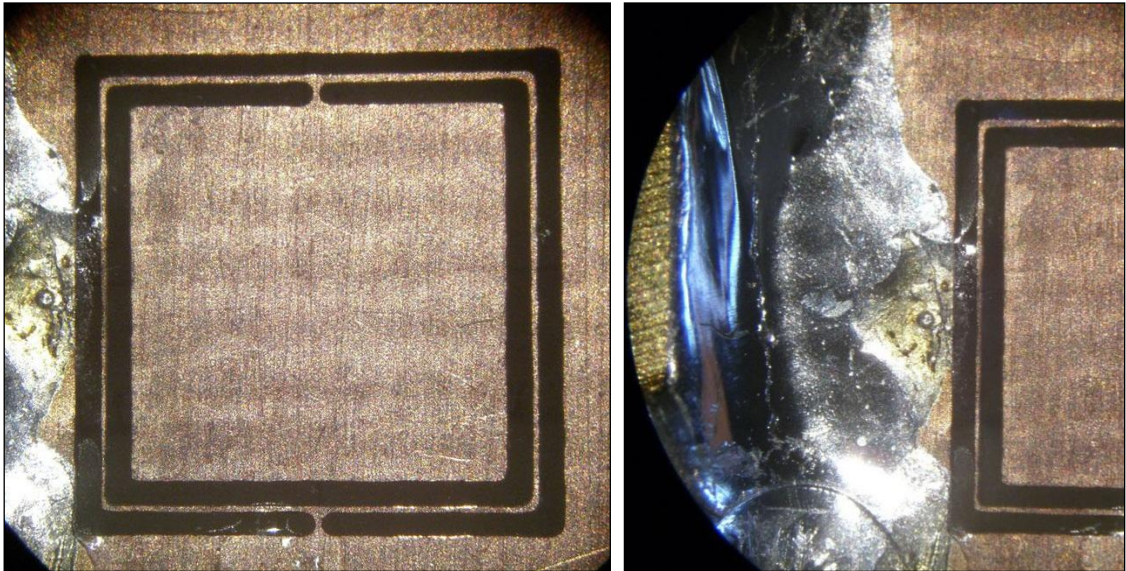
Detalle de un CSSR y una soldadura del circuito 4.
